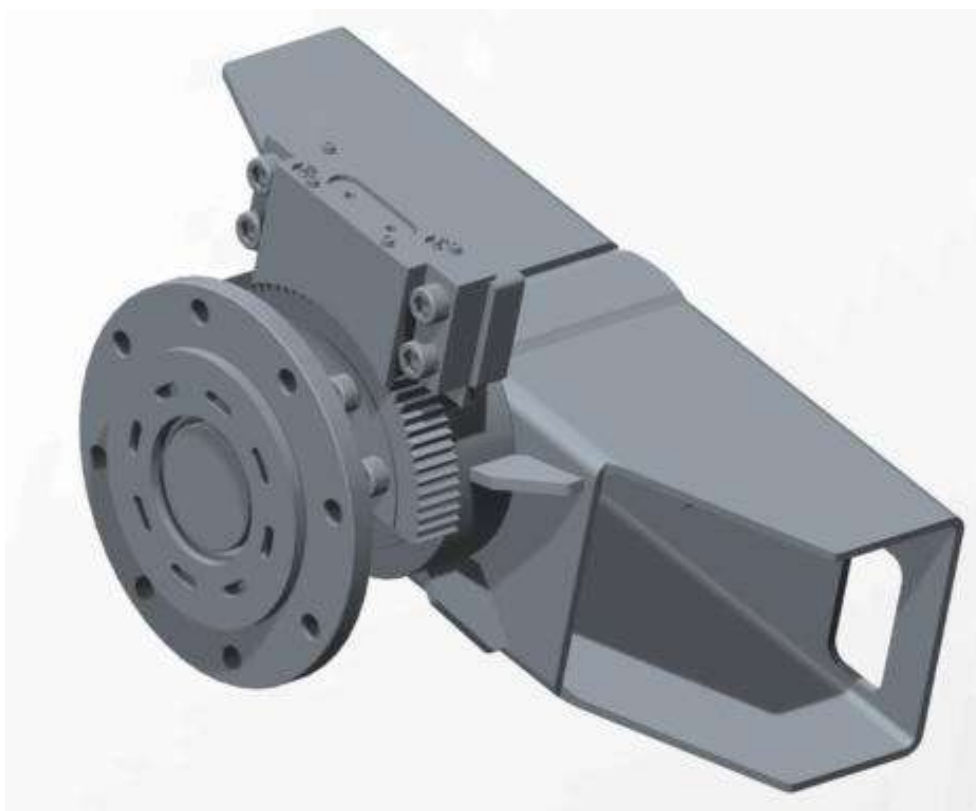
Středový otočný díl lesní vyvážecí soupravy
